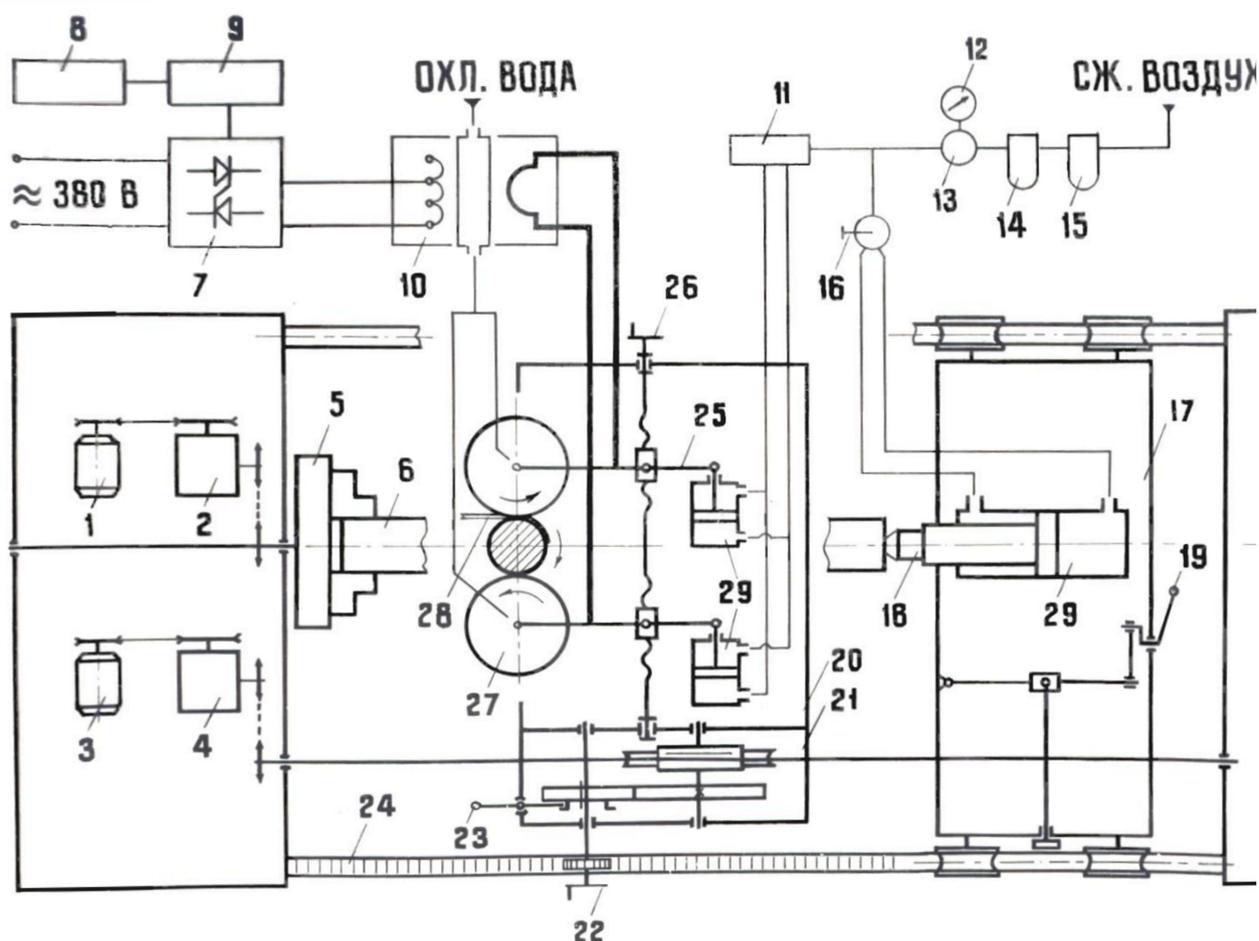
Схема установки 011-1-10 для электроконтактной приварки:
